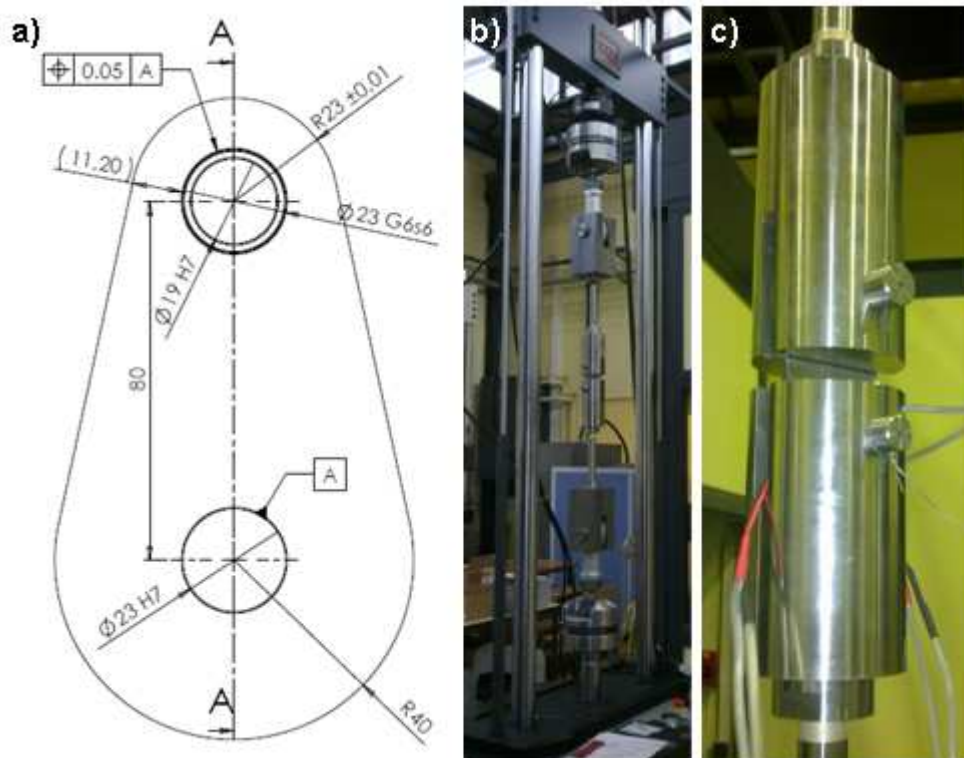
a) Plan de la manille en Inconel 718 équipée d'une bague en Inconel 718, b) Vue d'ensemble du montage d'essai, c) détail
